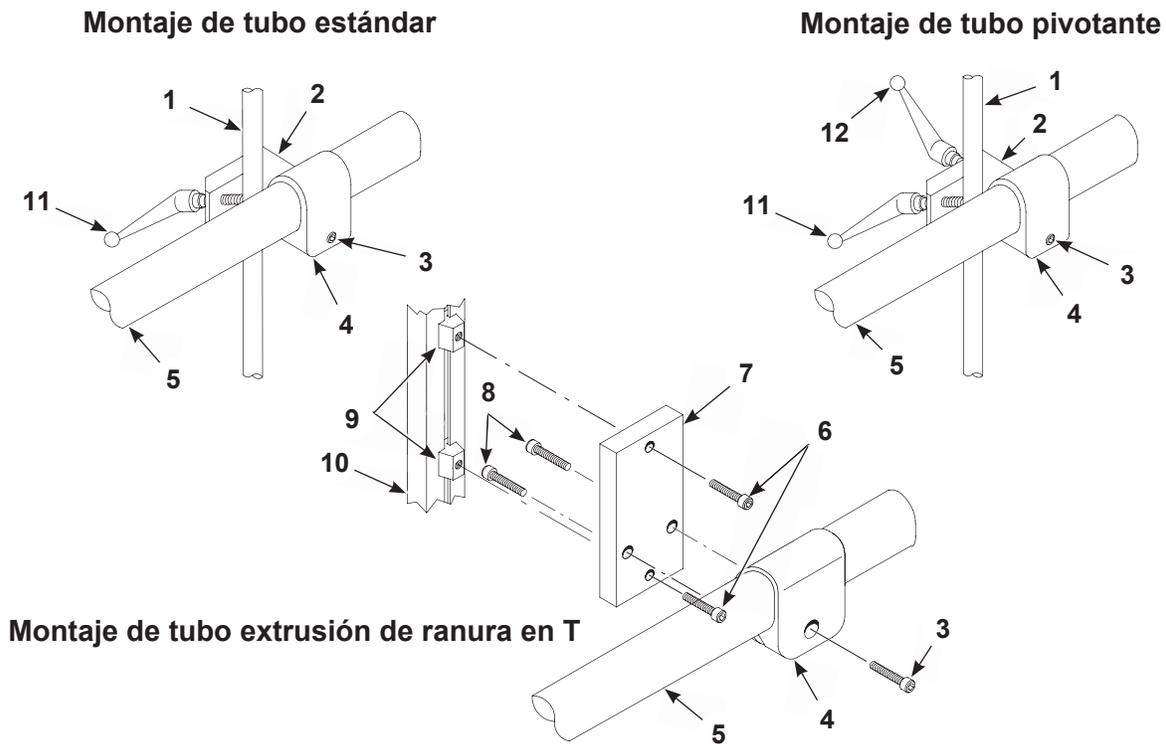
Montaje del kit de pistola de aplicación de montaje en tubo
